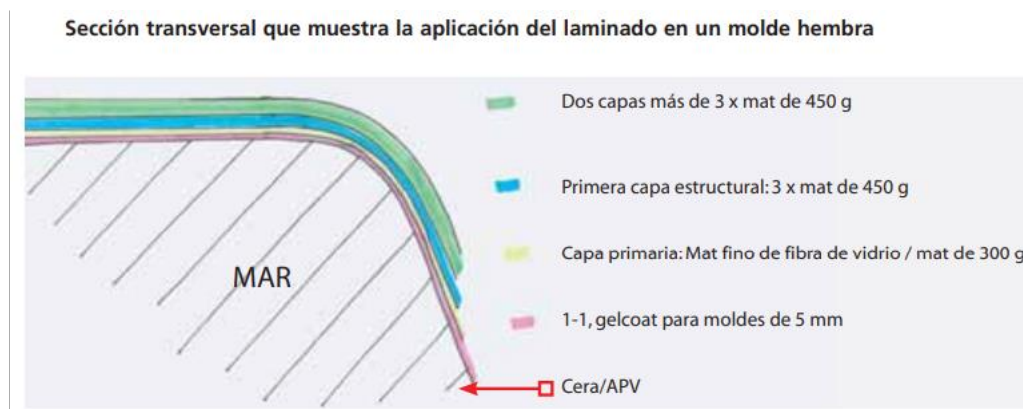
Aplicación laminado fibra de vidrio. Fuente: FAO
